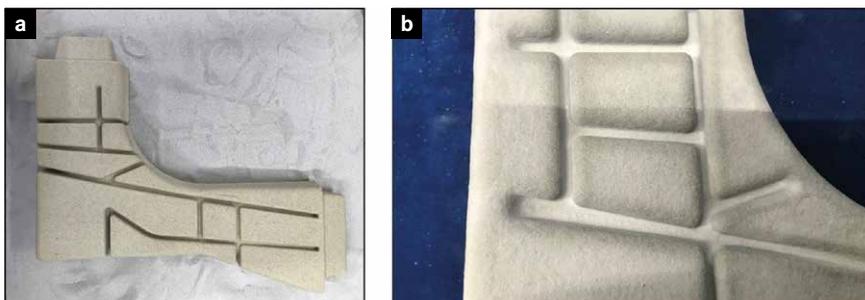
a) unbeschichteter Sandkern; b) höhere Vergrößerung der Oberfläche mit aufgetragener wasserbasierter Beschichtung.
